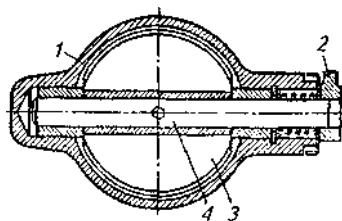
Моторный тормоз-замедлитель: 1 — корпус; 2 — поворотный рычаг; 3 — заслонка; 4 — вал
